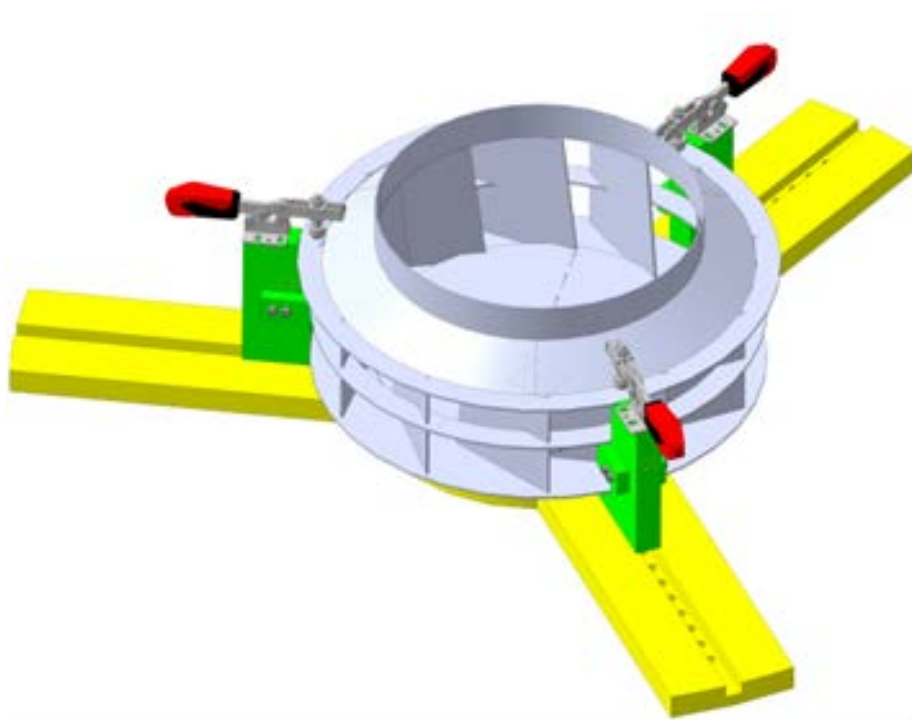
Приспособление для сборки рабочего колеса вентилятора
